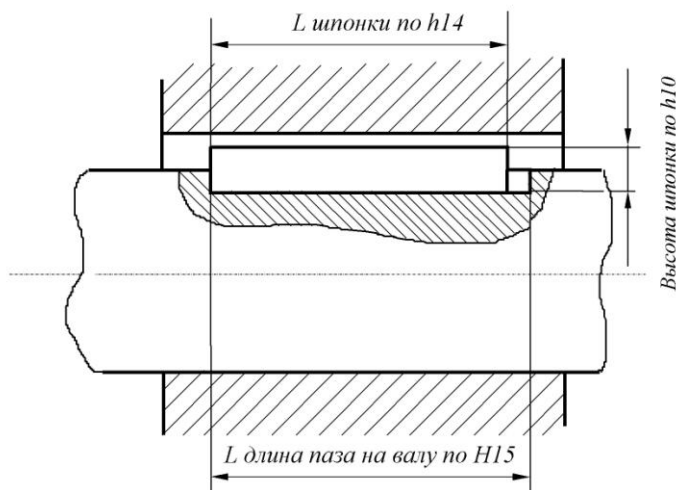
Поля допусков непасадочных размеров шпоночного соединения
